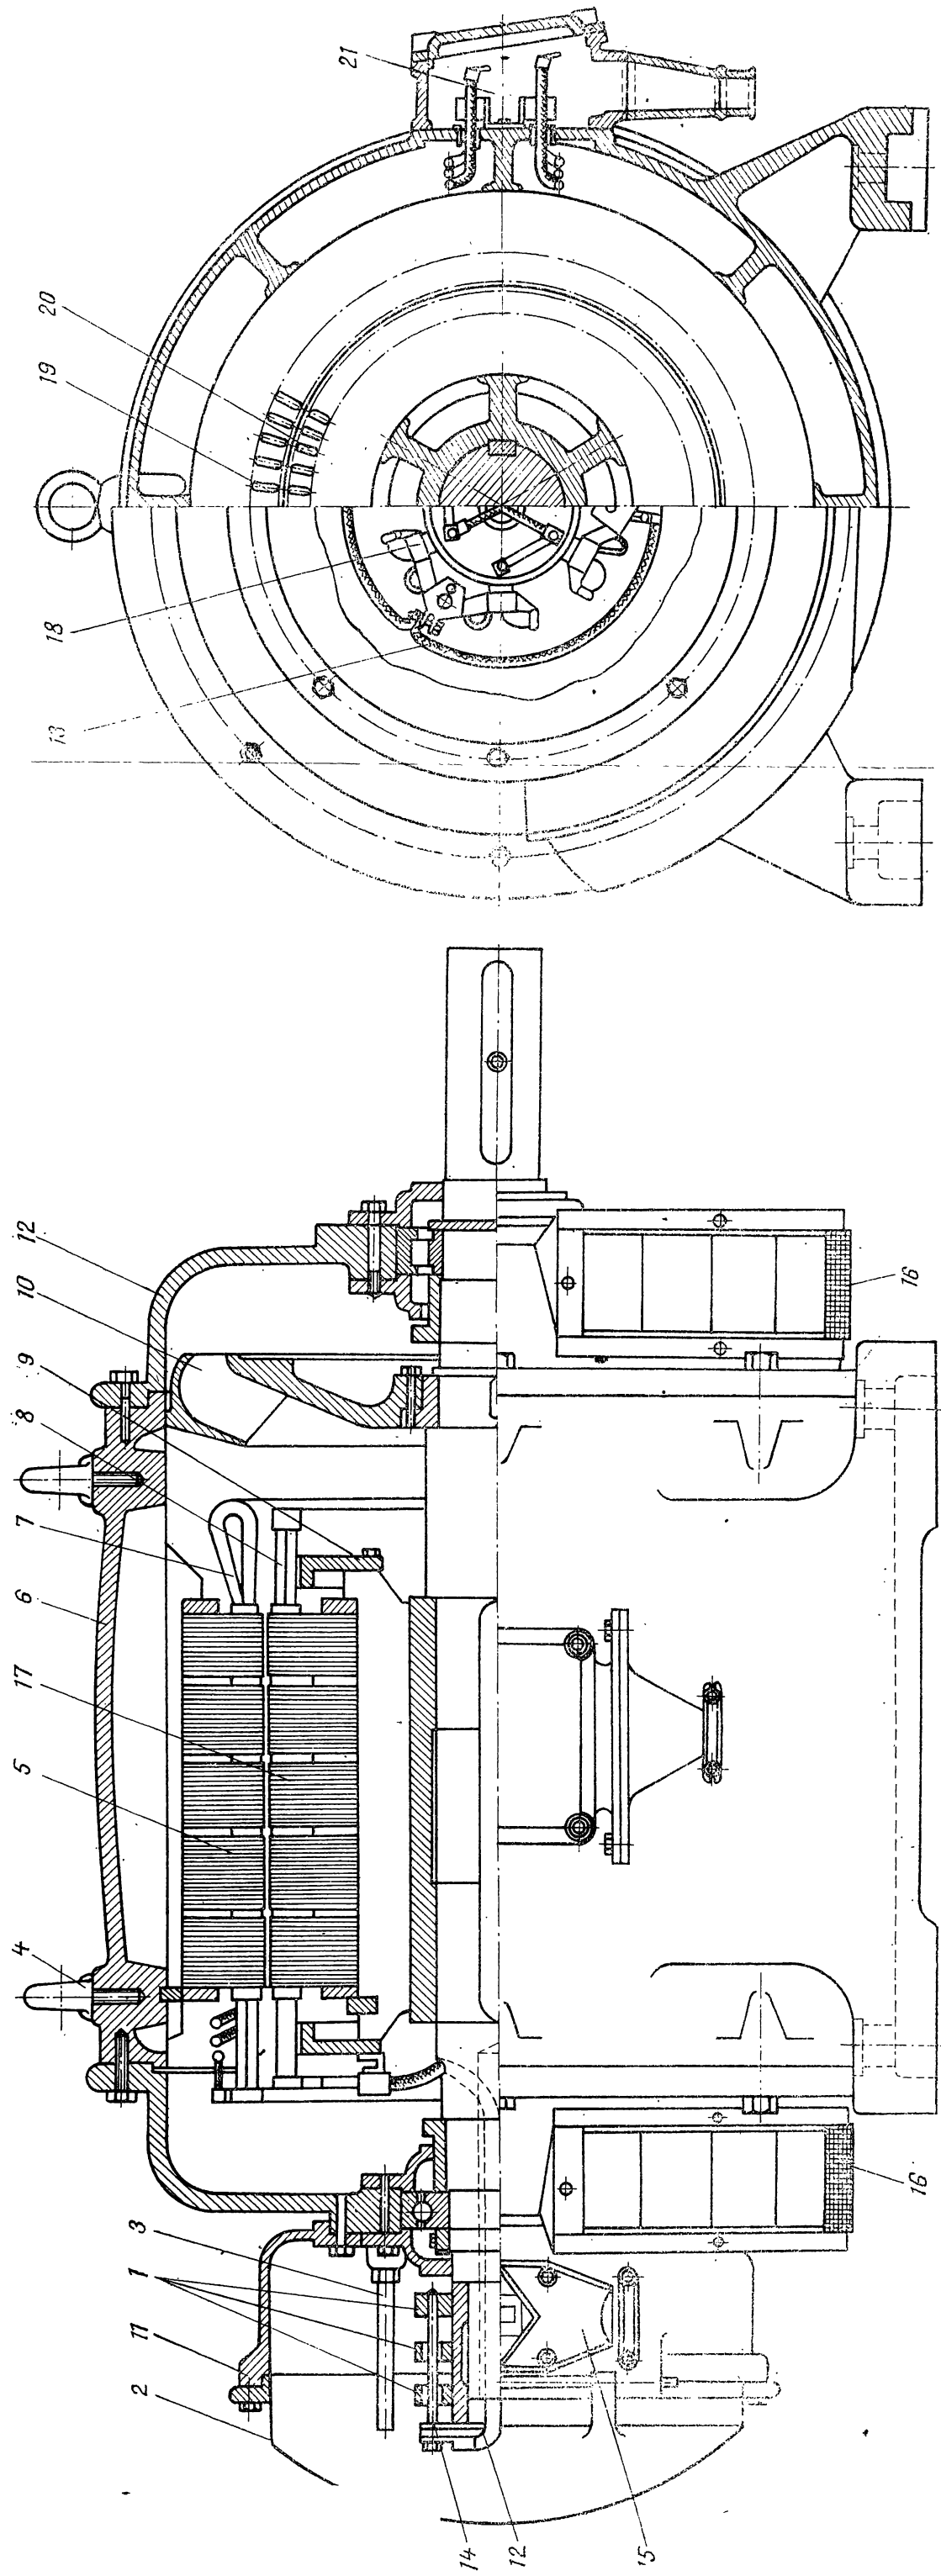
, B. Secțiune longitudinală și transversală printr-o mașină asincronă cu rotor bobinat
